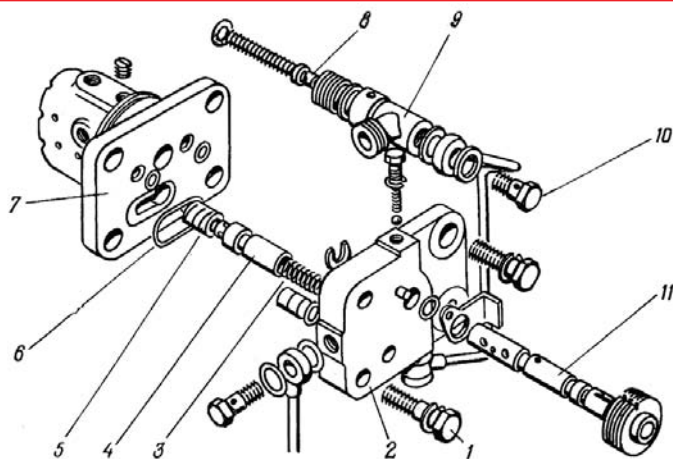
Взаимное расположение деталей при разборке датчика блокировки дифференциала: 1, 10 — болты; 2 — крышка; 3 — пружина; 4 — золотник; 5 — толкатель; 6 — кольцо; 7, 9 — корпуса; 8 — клапан; 11 — кран
